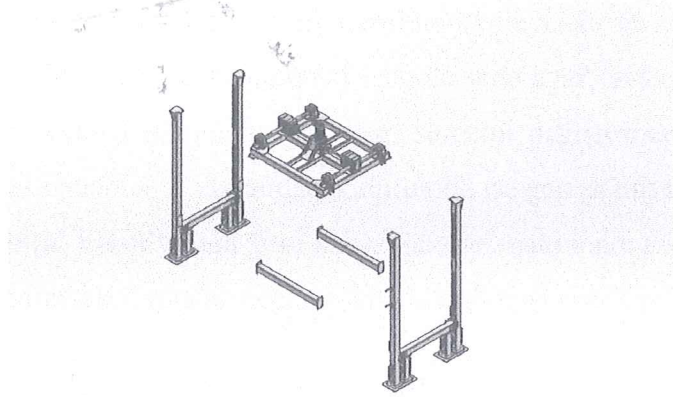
Üst tahrik sistemi izometrik montaj
